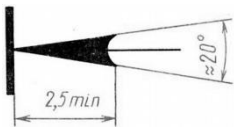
Форма размерной стрелки и размеры. Каждый размер на чертеже указывают только один раз.
